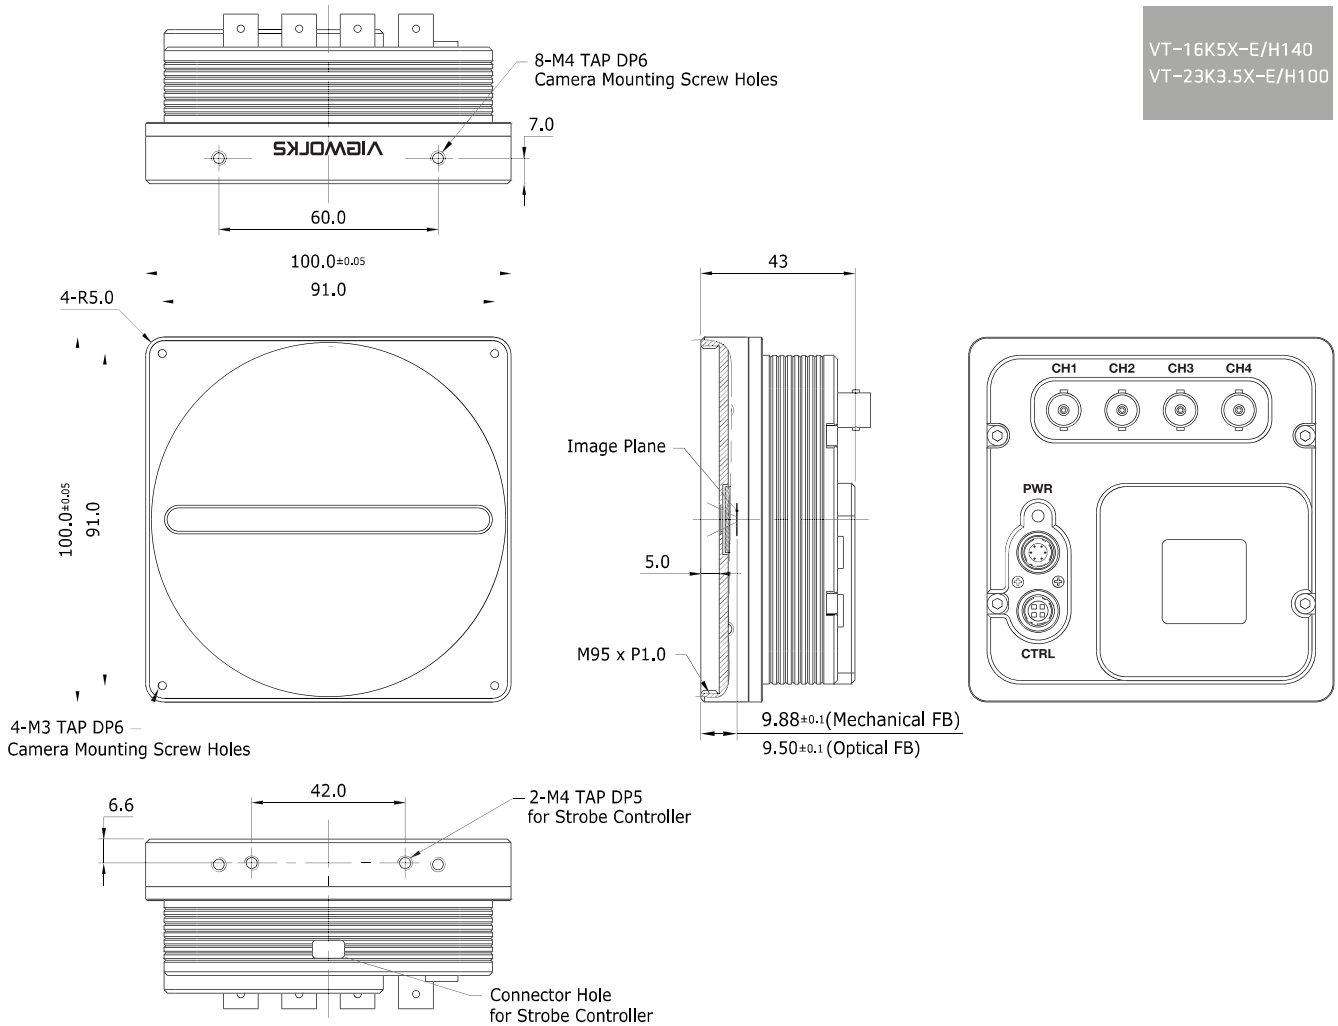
M95 mount 지원 VT CXP Series Mechanical Dimension
